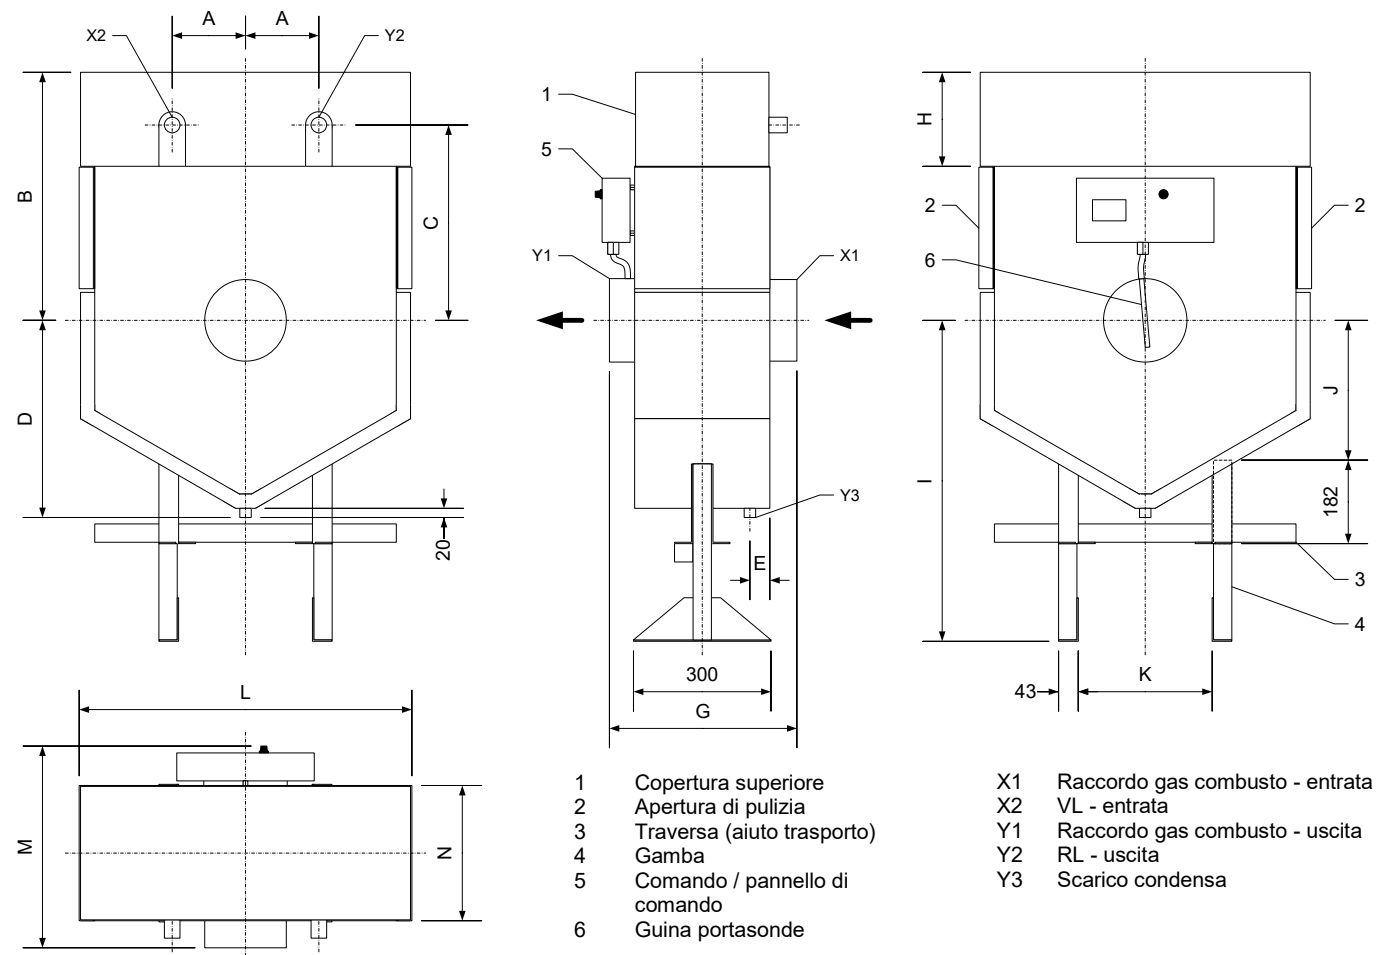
Dimensioni MX 90 - 250 (330 - 650)
